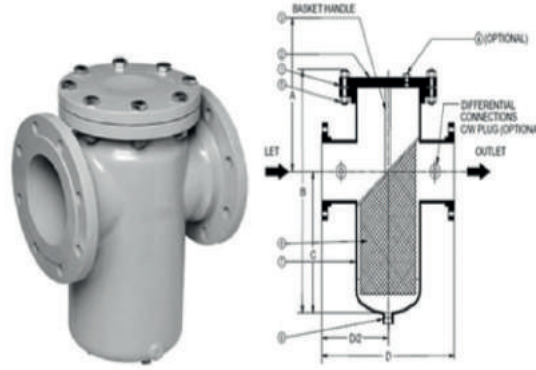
Sıvılar Uygulamaları Montaj Şekli
